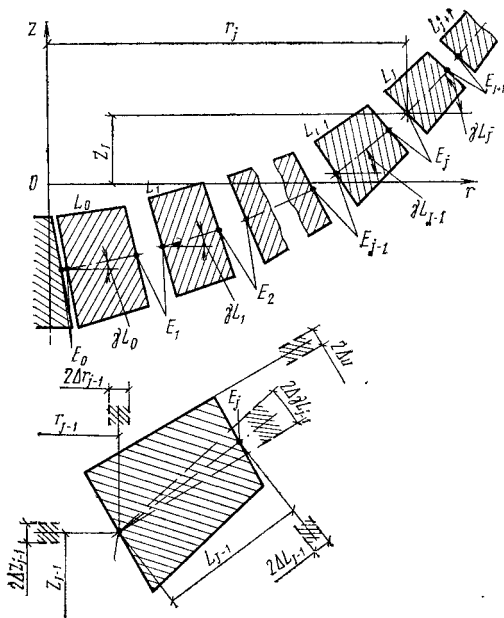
Размерная цепь при сборке зеркала без юстировки из блоков
